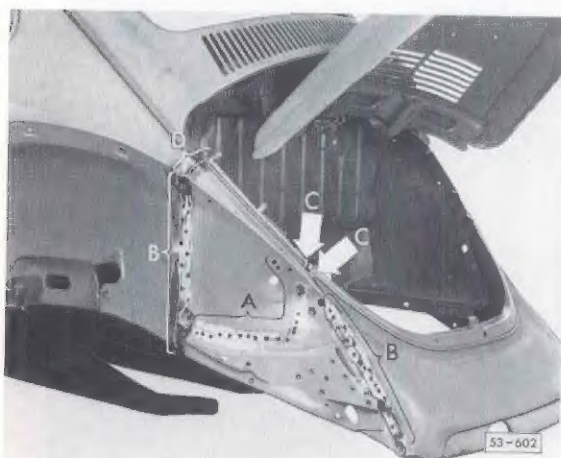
Seitenteil-Abschnittsteil, Motorabdeckblech und Anschlußblech hinten einschweißen.
